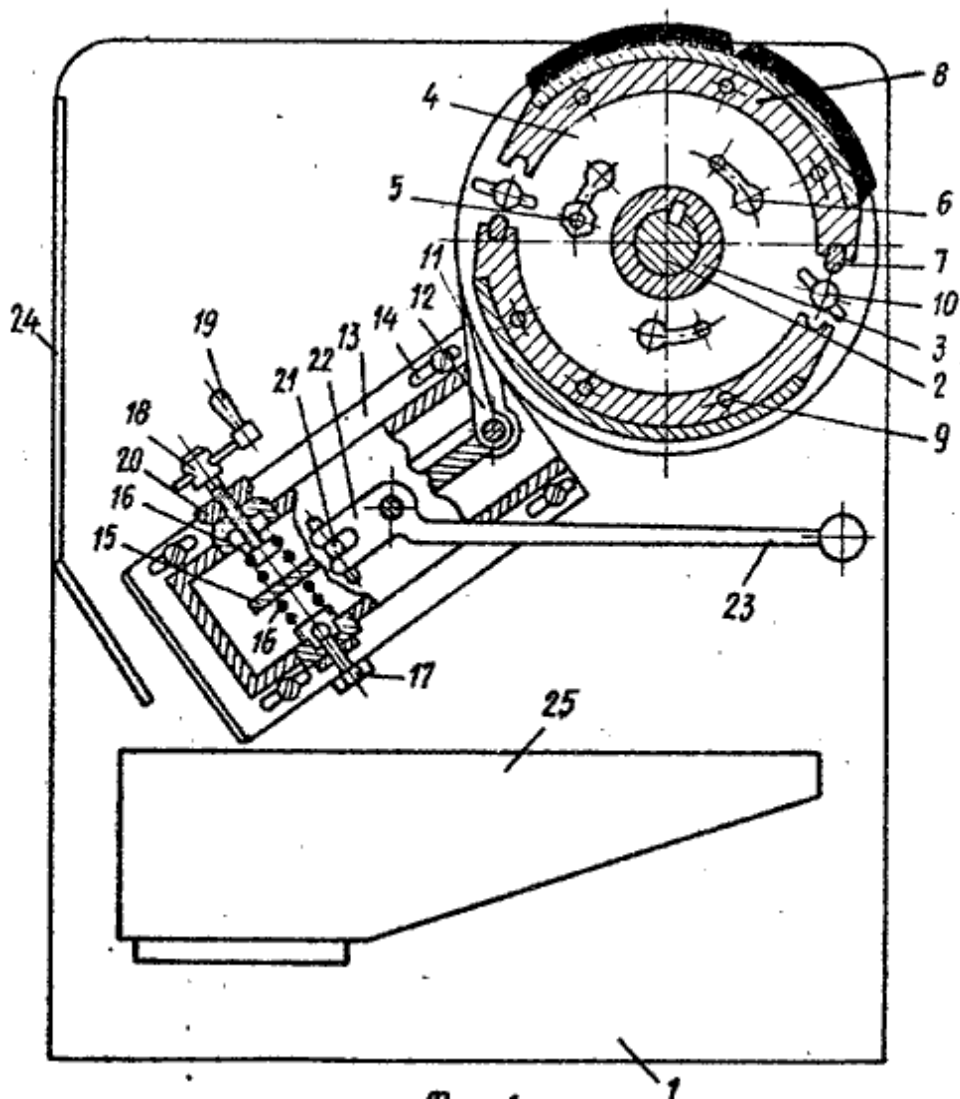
Общий вид станка (А.С. 1301585)
